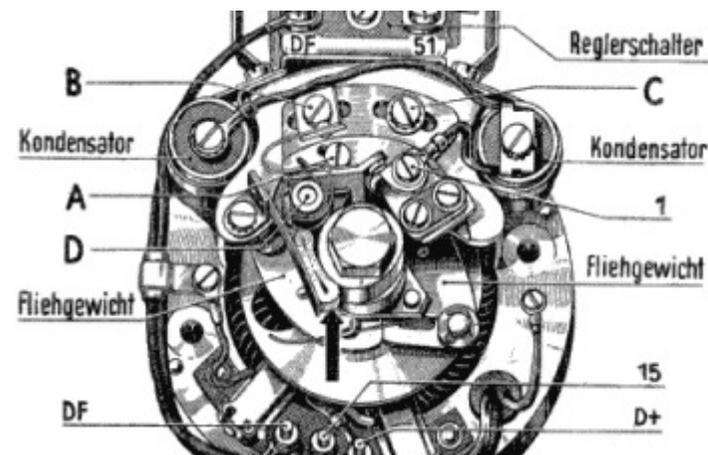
Lichtmaschine mit Fliehwichts-Zündversteller und Unterbrecher
